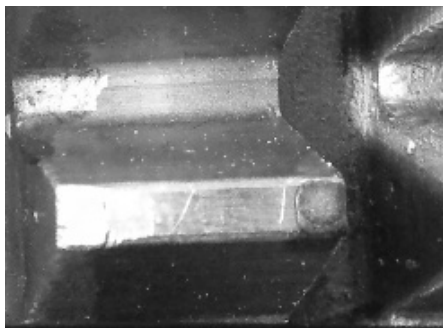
Фотография зуба фрезы из инструментальной стали P18K5Ф2, обработанного в режиме закалки без оплавления
